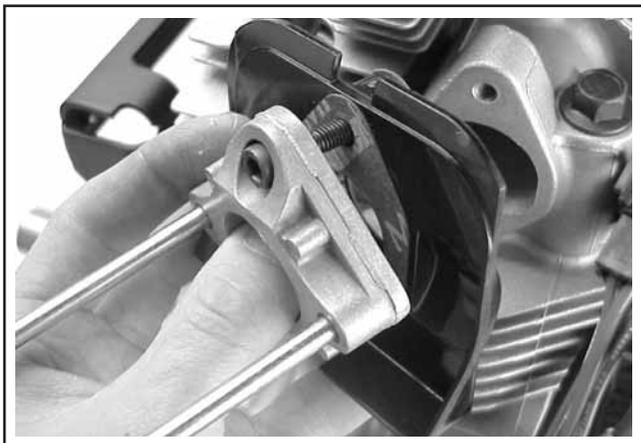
Retirar o Adaptador do Carburador e o Deflector de Aquecimento.
